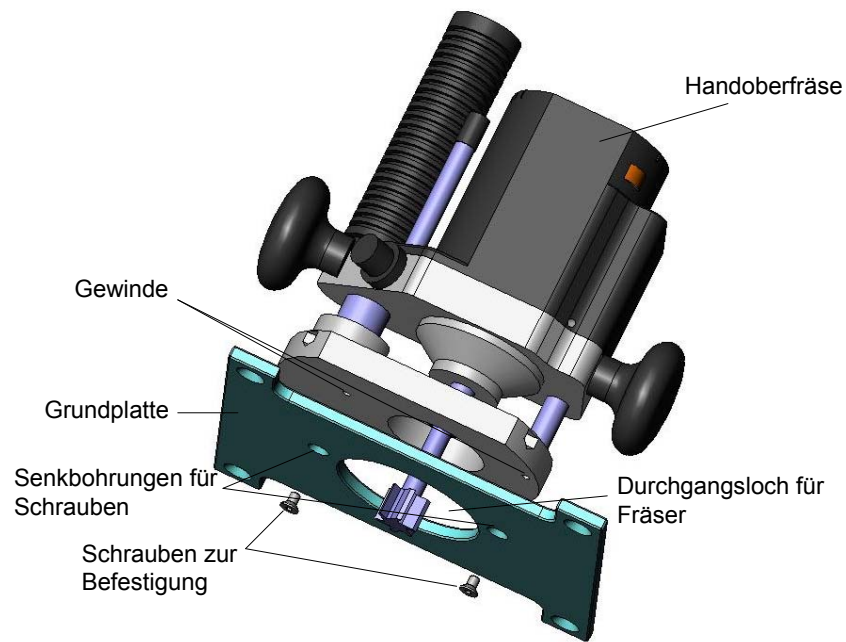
Befestigung der Handoberfräse auf einer Grundplatte
